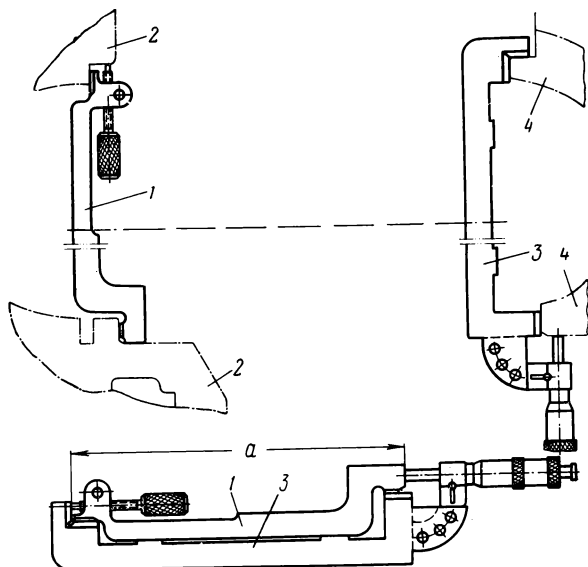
Приспособления для определения размеров a пазов у остова и выступов у букс:
